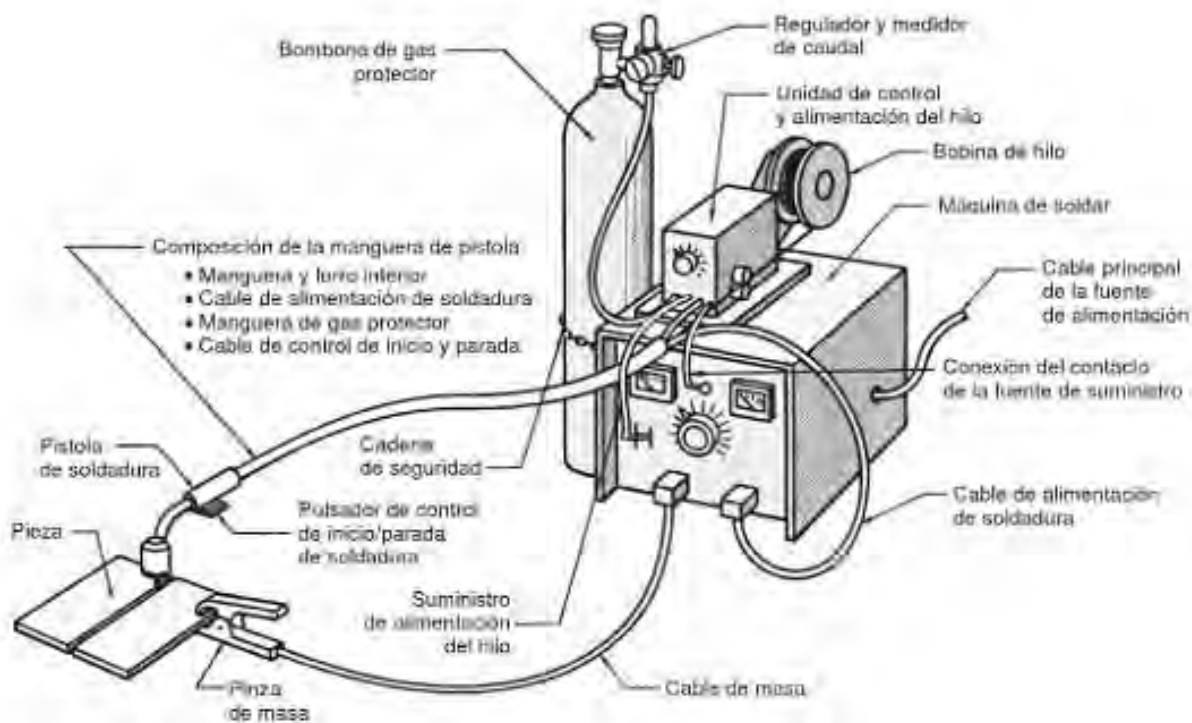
Proceso de soldadura GMAW<sup>5</sup>
